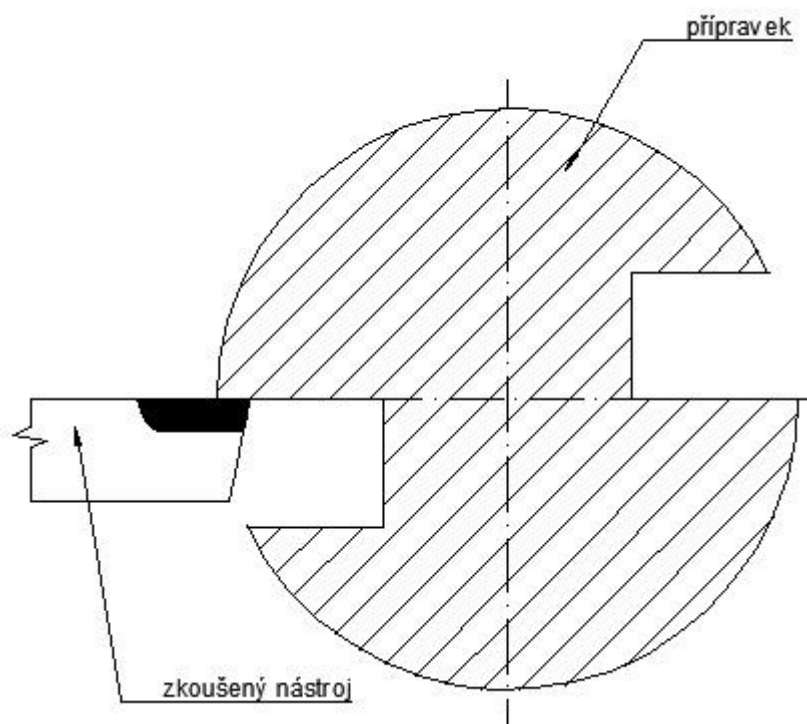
Schéma přípravku pro podélné soustružení přerušovaným řezem
